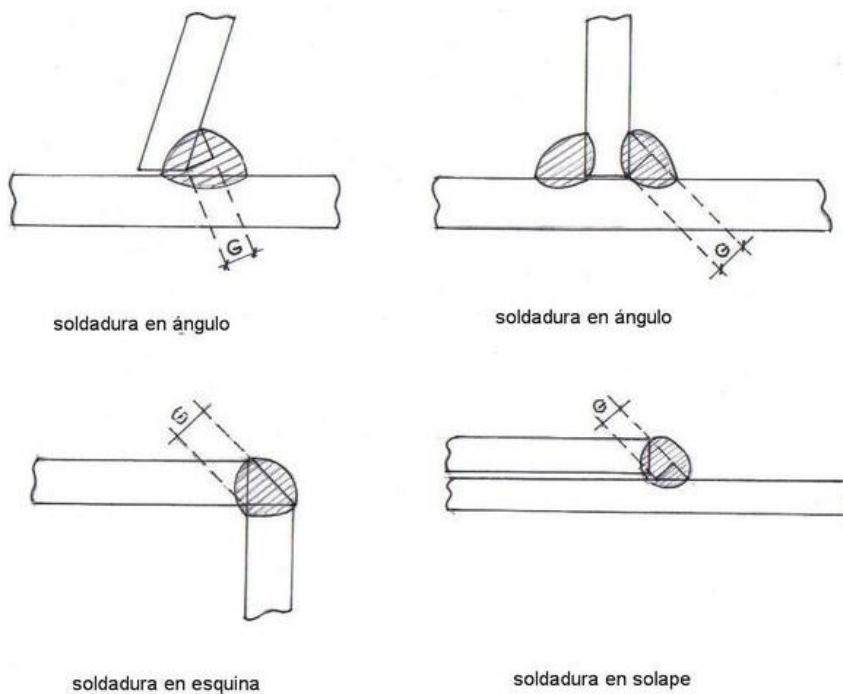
Cordón de soldadura en ángulo G .
